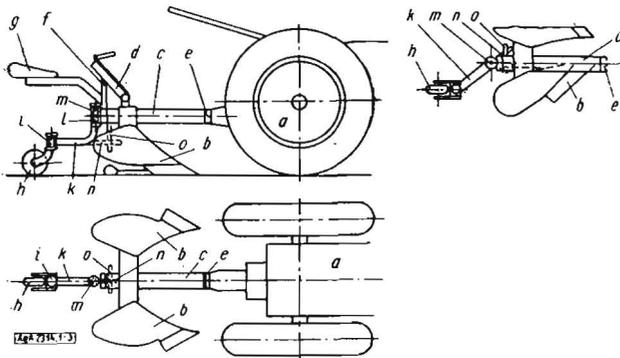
Anbaudrehpflug mit einem Einachsschlepper gekuppelt (Seitenansicht)
